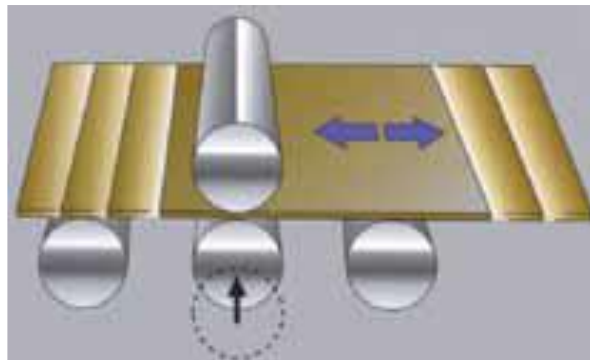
Montaje de la chapa en la máquina de 4 rodillos
